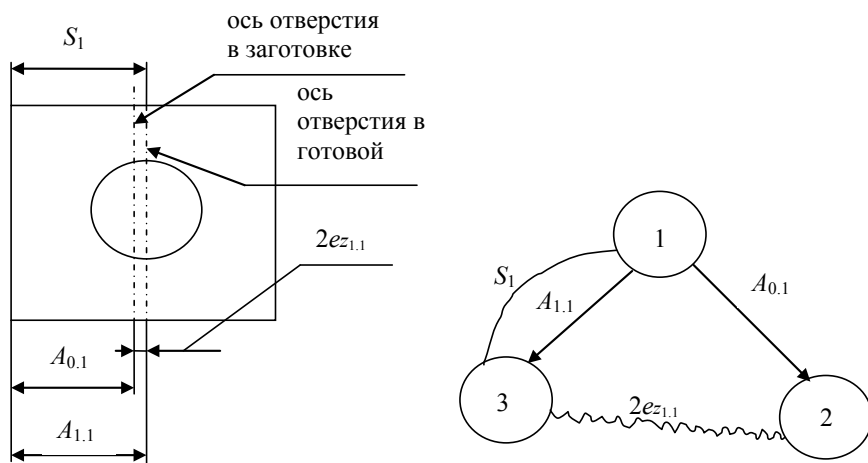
Схема обработки и граф размерных связей для детали с отверстием
